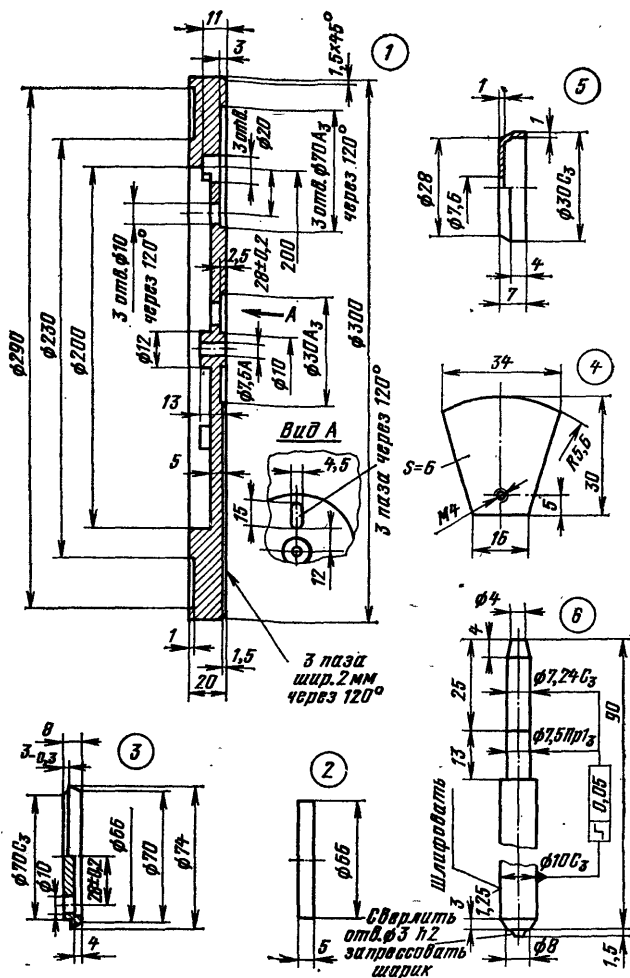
Детали диска сверхтихоходного электродвигателя для ЭПУ.
